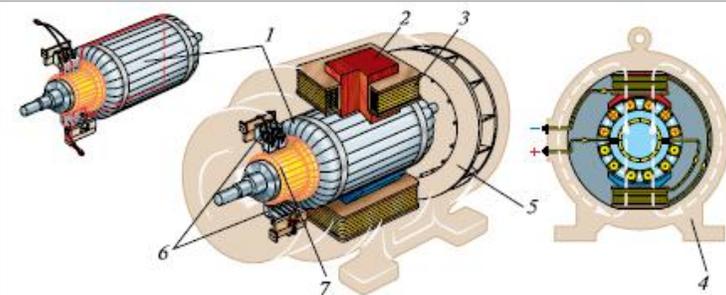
Схема коллекторного двигателя: 1 — якорь; 2 — сердечник полюса; 3 — обмотка полюса; 4 — статор; 5 — вентилятор; 6 — щётки; 7 — коллектор
